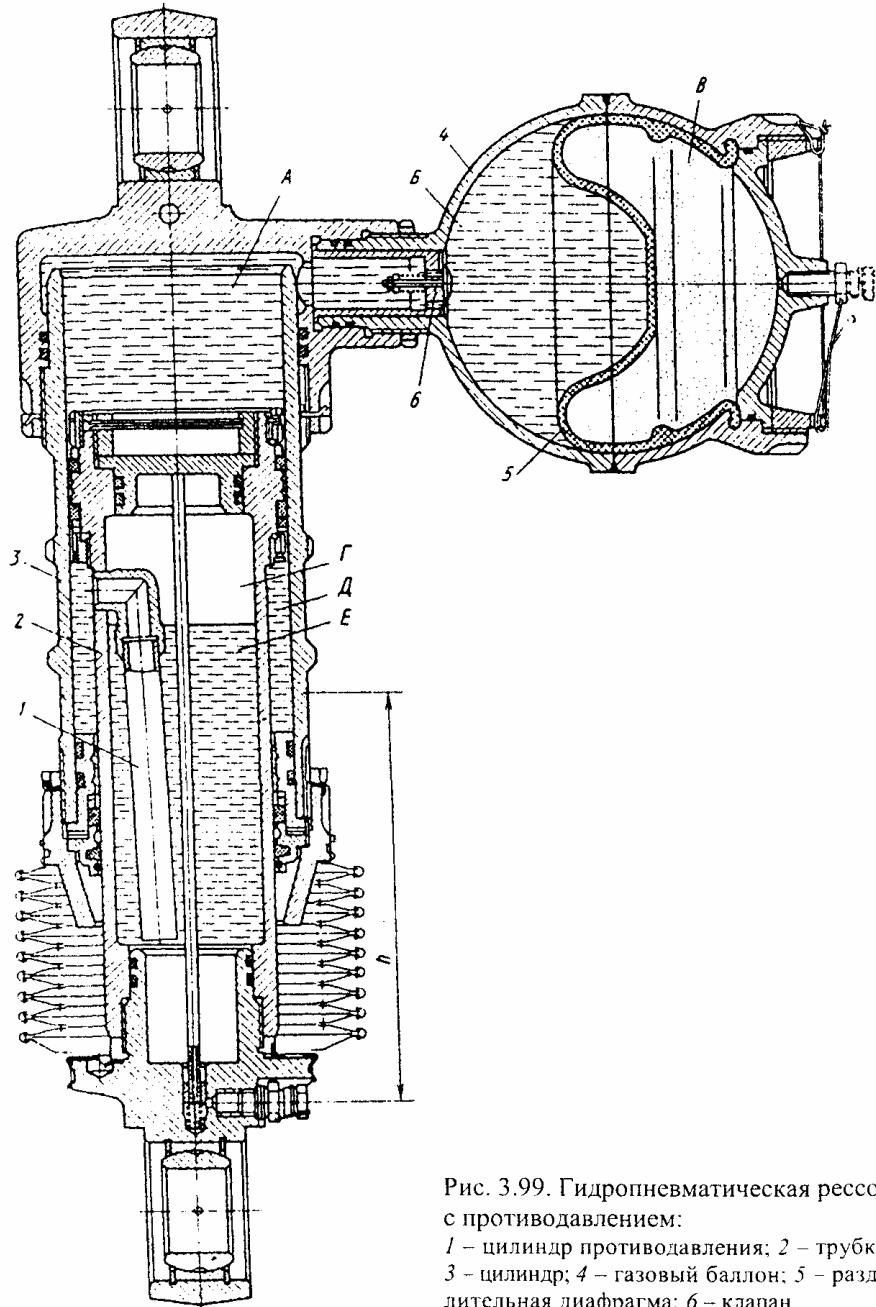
Гидропневматическая рессора с противодавлением:
